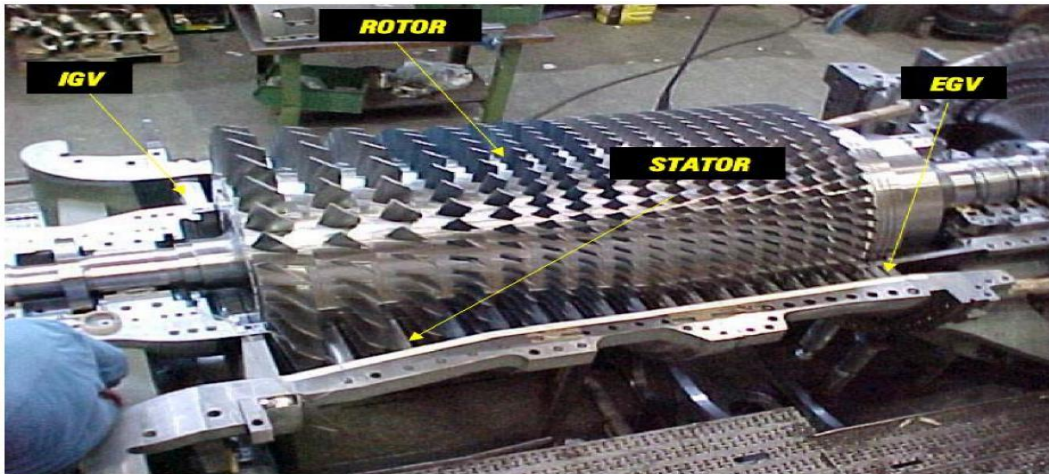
Compresseur axial ; IGV : Inlet Guide Valve ; EGV : End Guide Valve
